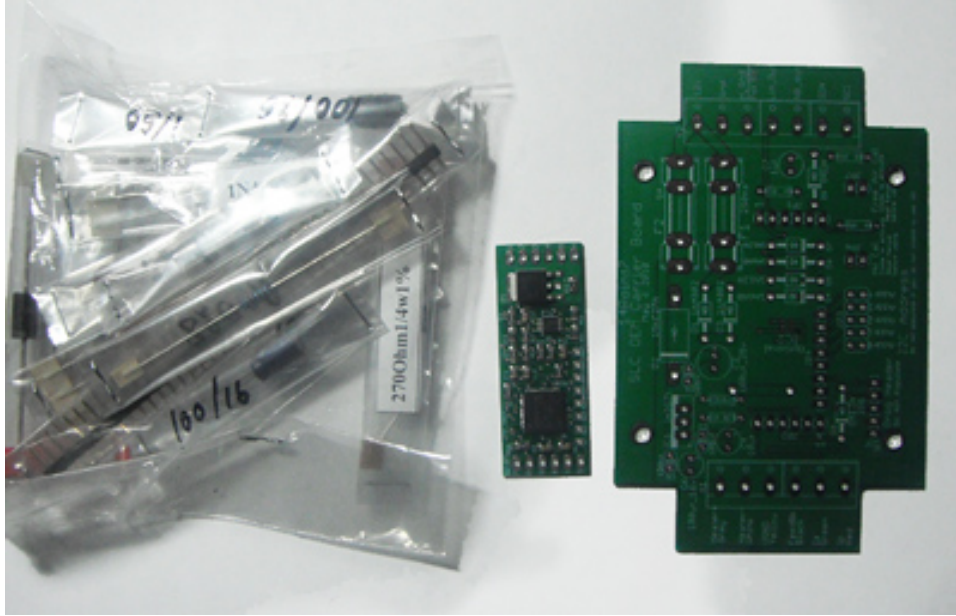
Tarjeta de control del sensor de oxígeno antes de soldar
